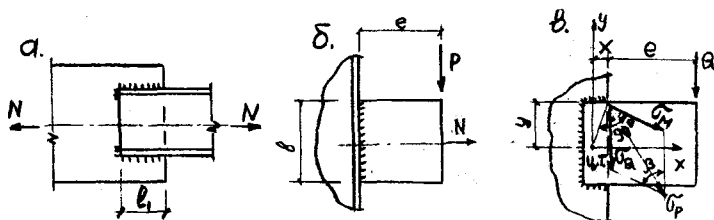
Схемы сварных соединений с угловыми швами
